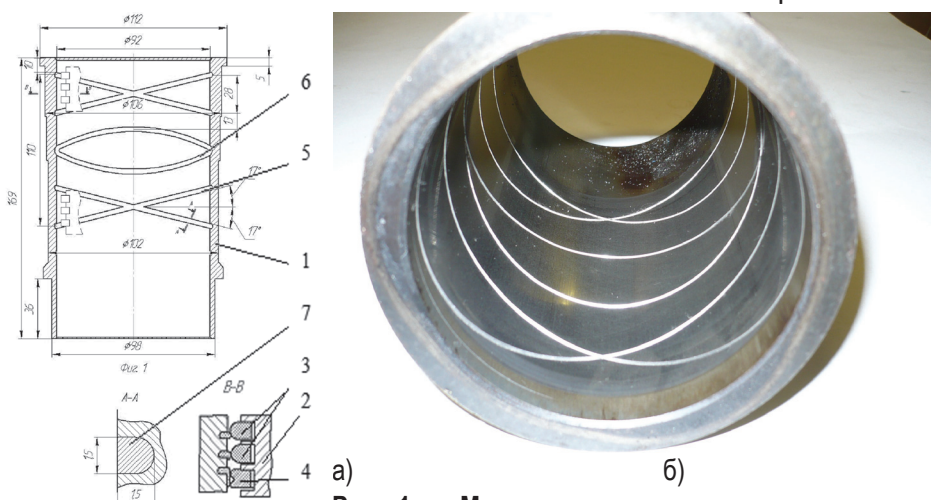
Модернизированная гильза цилиндра двигателя УМЗ-417: а) схема расположения канавок; б) общий вид
